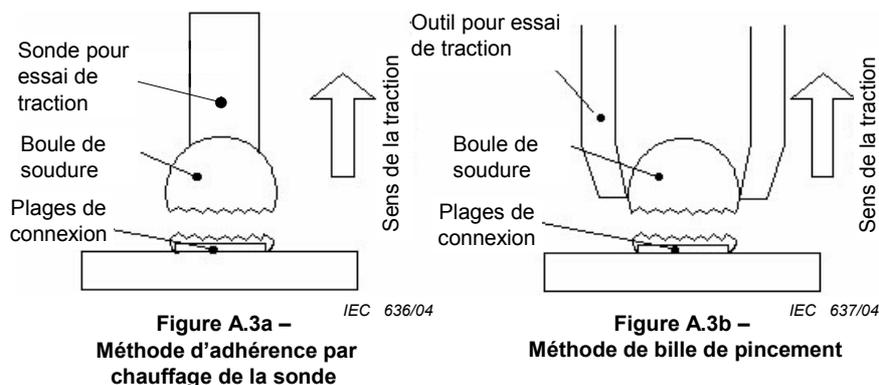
Méthode de mesure de la force d'adhérence des boules de soudure
